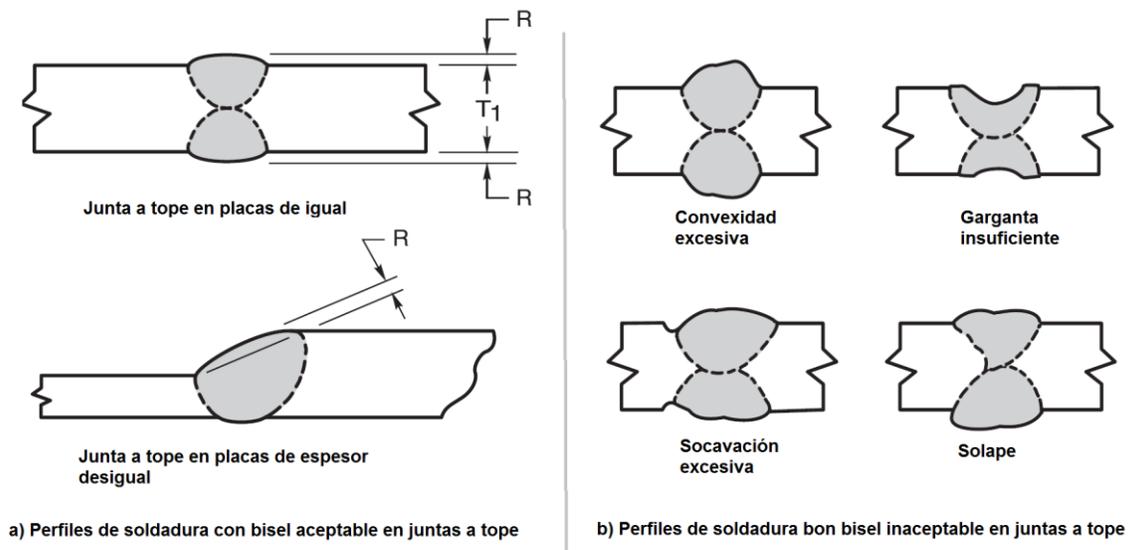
Perfiles aceptables e inaceptables de soldadura en juntas a tope.
